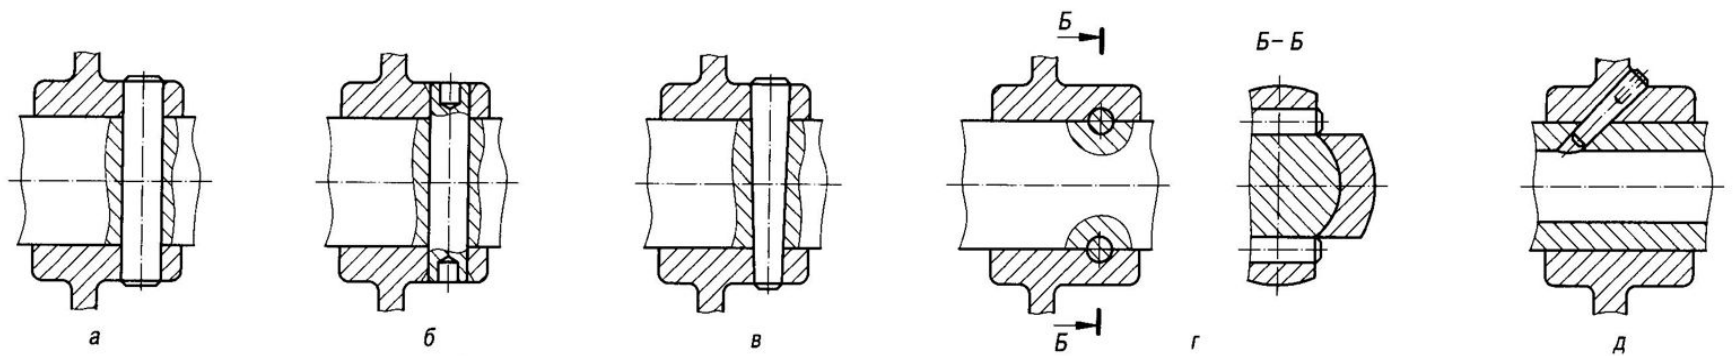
Способы фиксации деталей (а–д) с цилиндрическими поверхностями контакта
